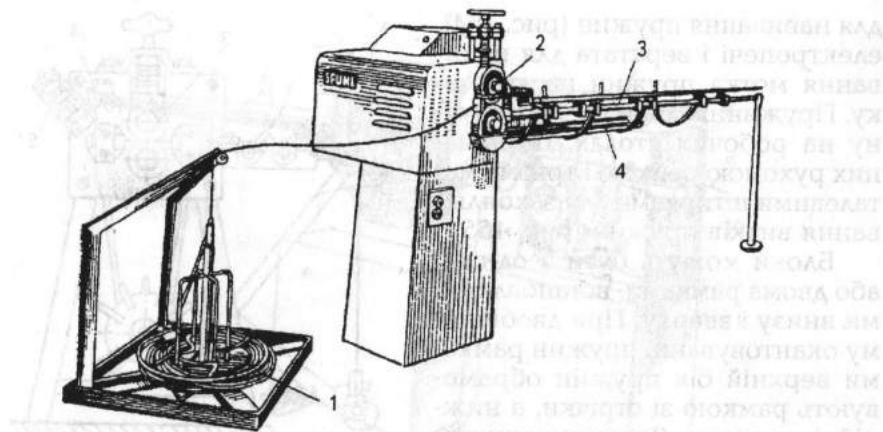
Верстат для з'єднання двоконусних пружин в пружинні блоки:
